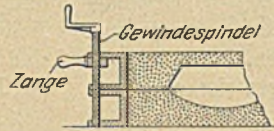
Einführung der Gewindespindel mit Zange zum Abheben des Umschlag-Oberkastens vom Unterkasten.
